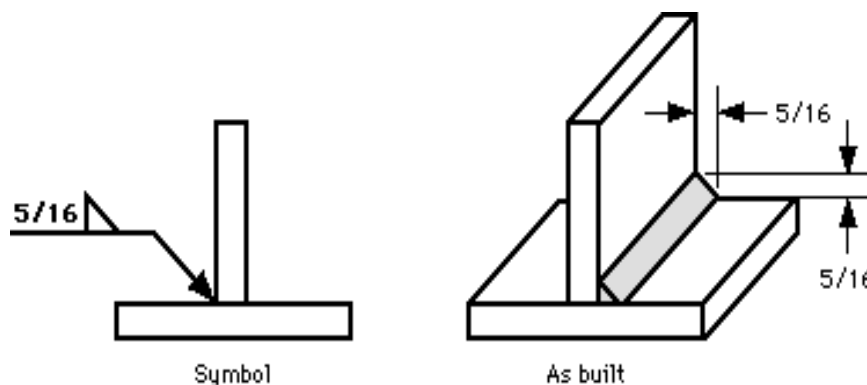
Soldadura de Filete (Caras Iguales).<sup>16</sup>
